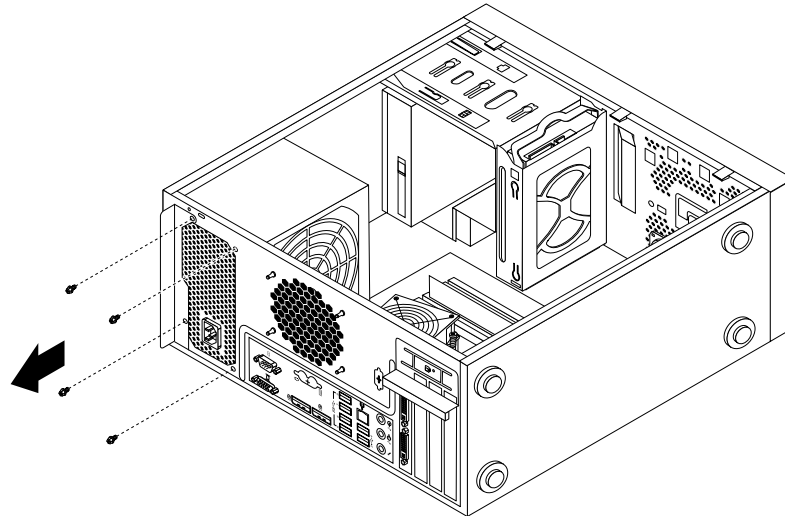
Schrauben entfernen, mit denen das Netzteil gesichert wird
